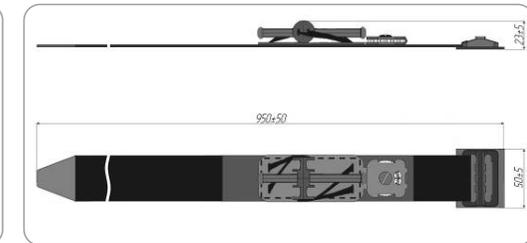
Внешний вид и габаритные размеры ЖК-02
